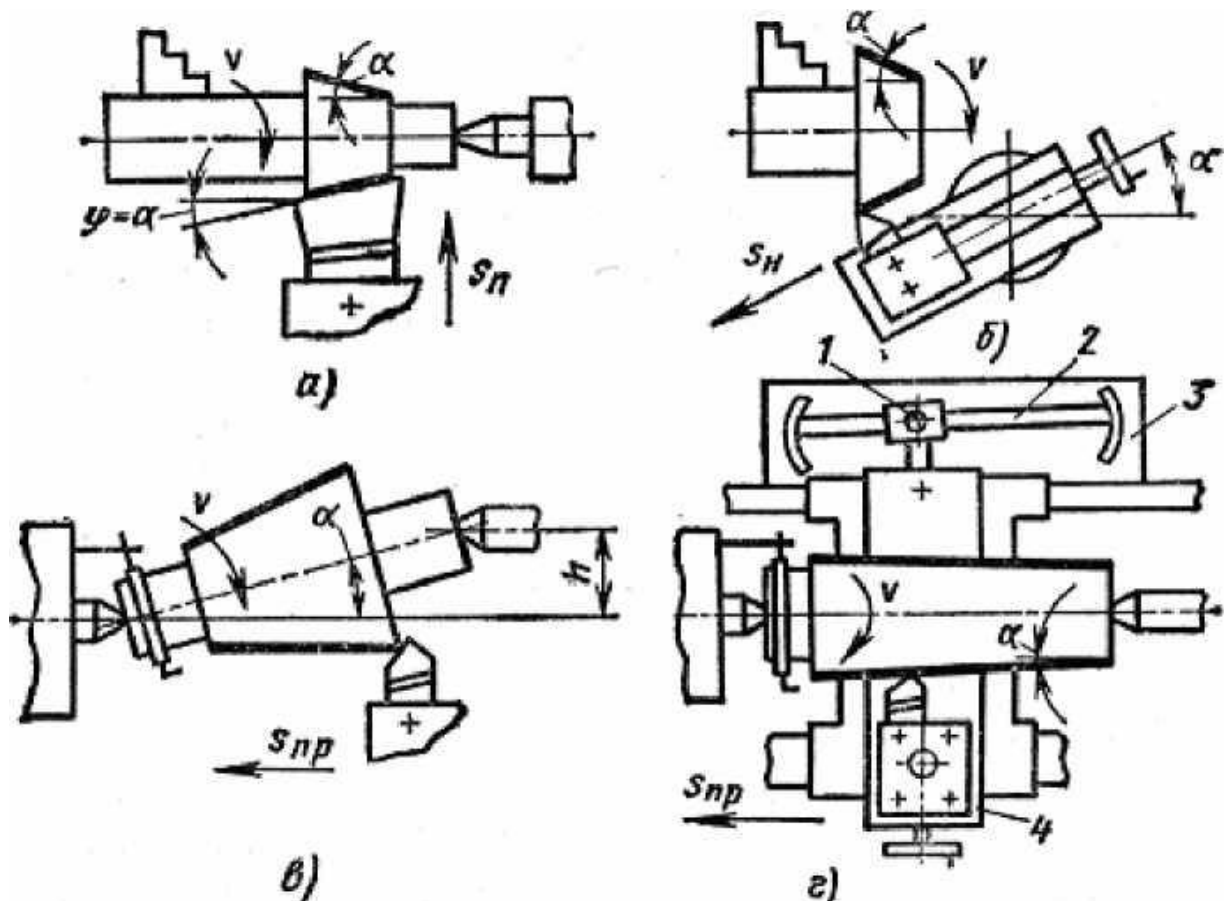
Схемы обтачивания наружных конических поверхностей на токарном станке: а - широким резцом; б - поворотом каретки верхнего суппорта; в - смещением корпуса задней бабки; г - с помощью копировальной конусной линейки
